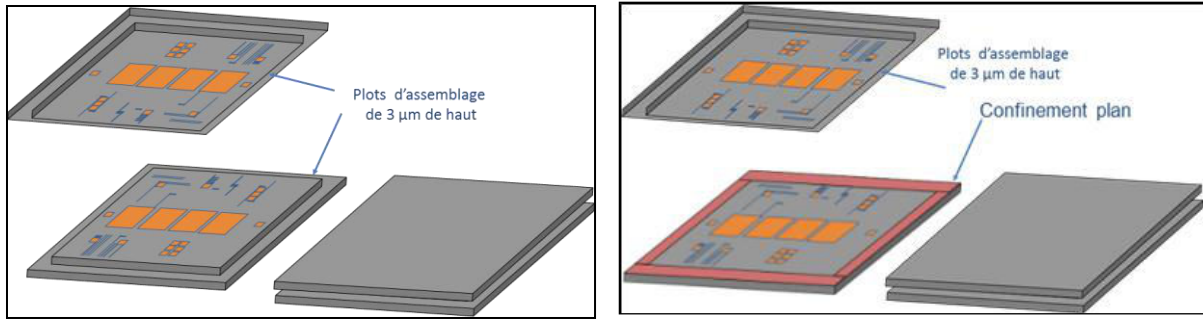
Les différentes configurations d'assemblage. A gauche, un assemblage plot-à-plot (3 µm). A droite, un assemblage plot (3 µm) à plan.
